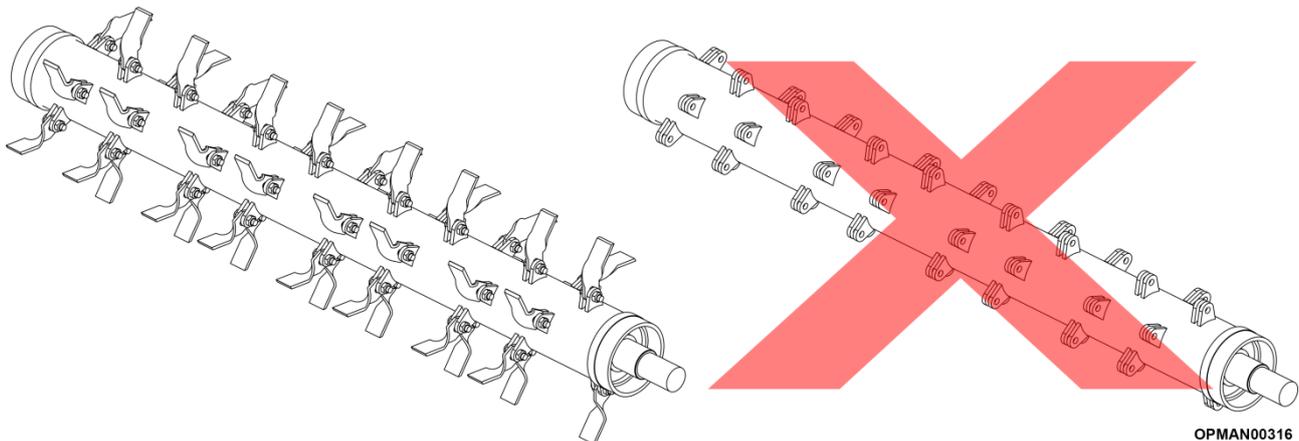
Lieferung eines kompletten Schlegelrotors mit Schlegeln von Spearhead
